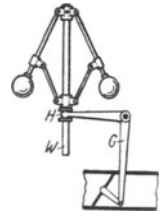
Zentrifugalregulator einer Dampfmaschine.
